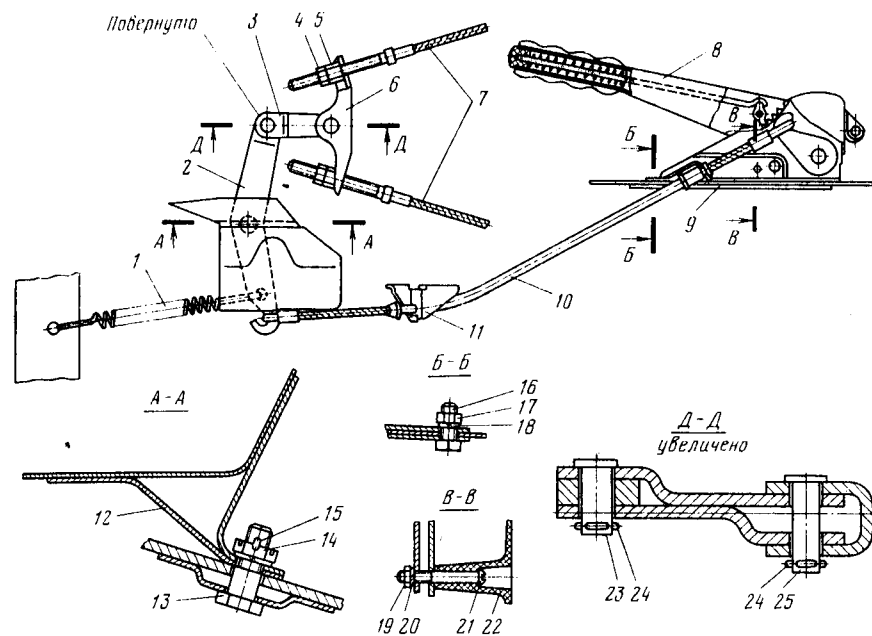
Установка ручного привода тормозных механизмов на автомобиле:
